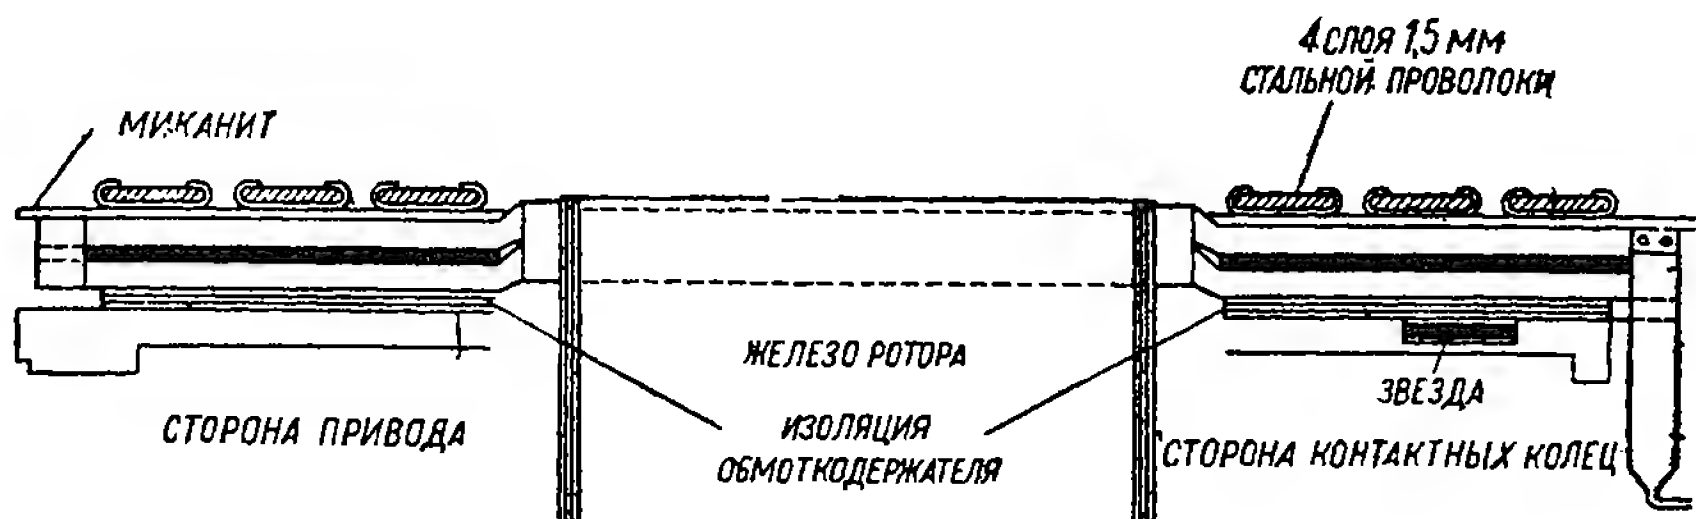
Обмоткодержатель ротора на 3000 об/мин.
